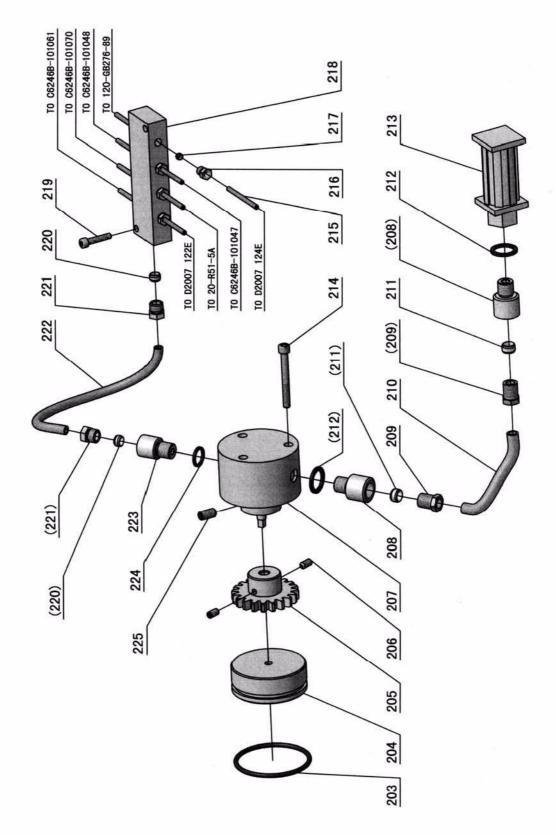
Spindelstock 8 von 8 - Headstock 8 of 8
